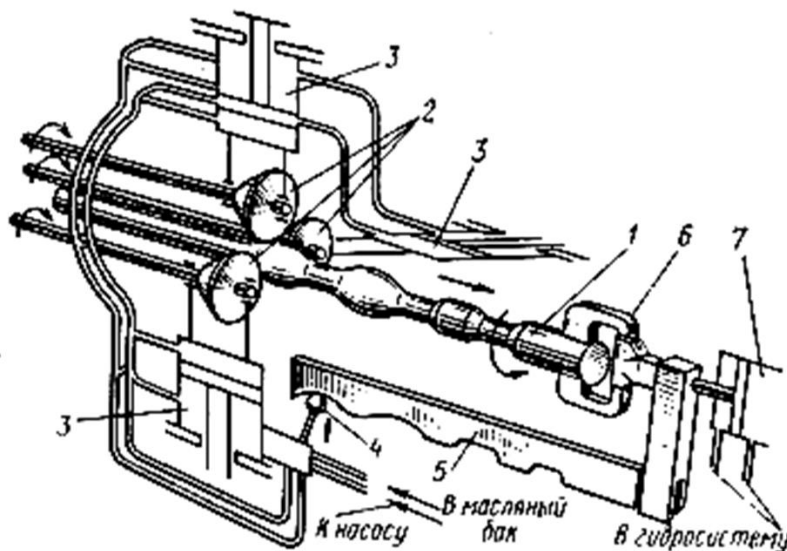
Схема поперечно-винтовой прокатки: 1 – заготовка; 2 – валки; 3, 7 – поршневые гидроприводы; 4 – шуп; 5 – копир; 6 – механическая рука
